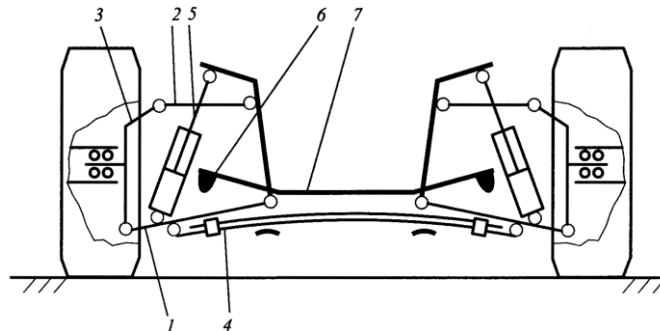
Схема передньої підвіски з поперечною ресорою двоточкового кріплення:
